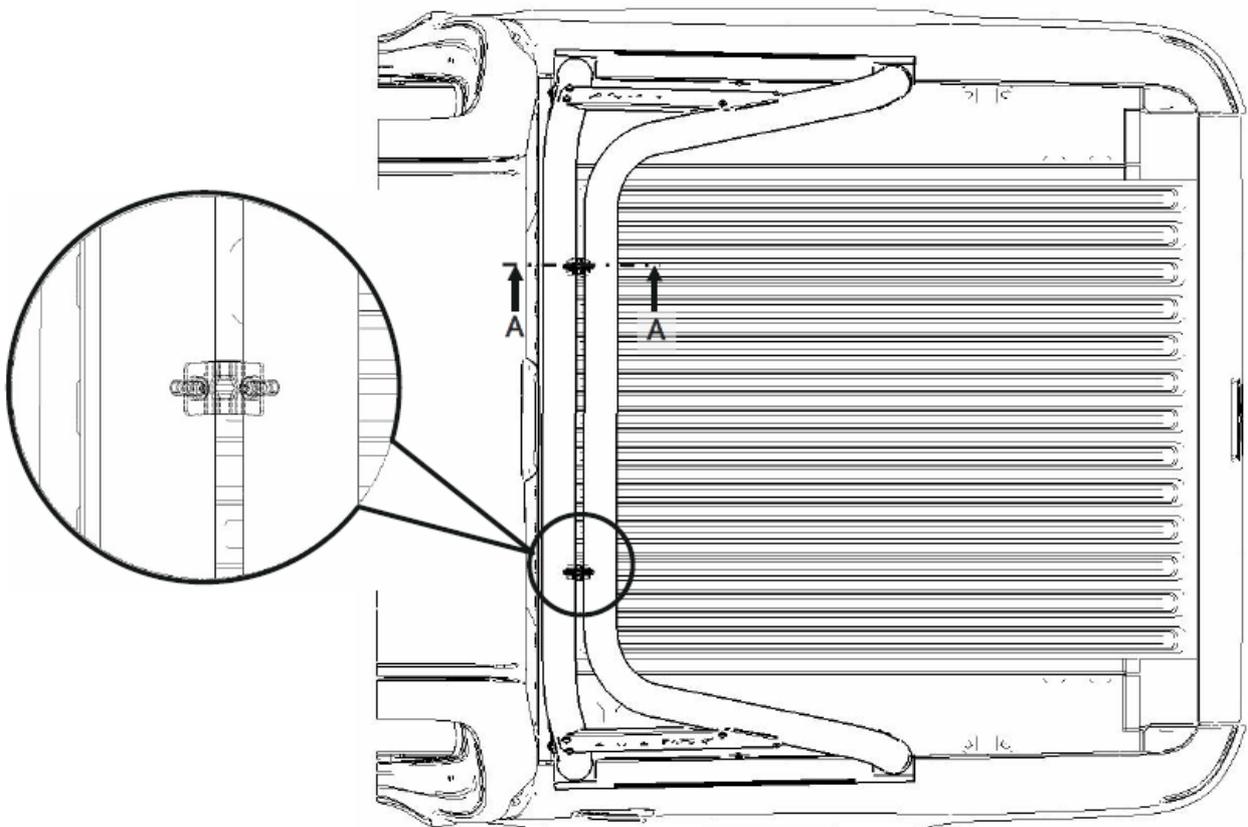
exemple de styling bar à deux tubes (vue de dessus)
